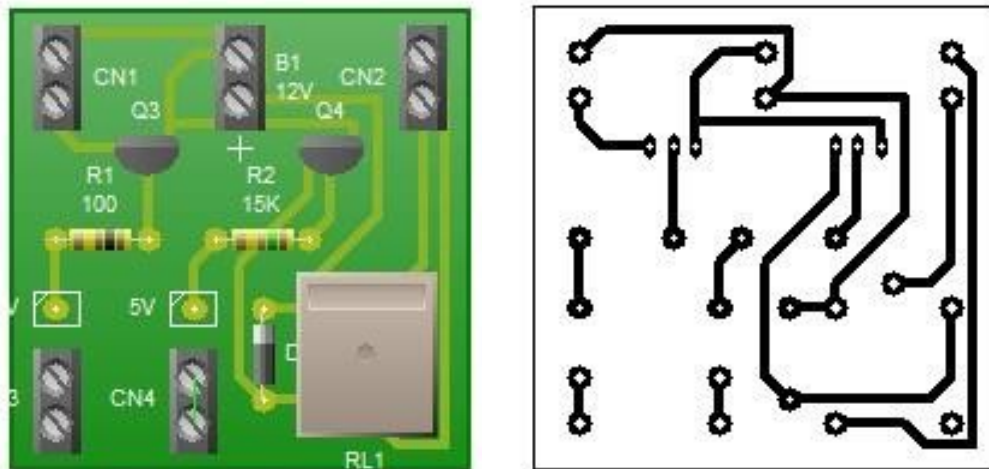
Placa PCB para instalación. (Imagen de autoría propia)
